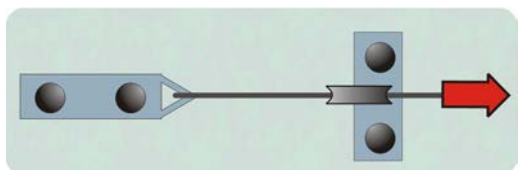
Hauptgruppen-Formen (Wellenhofer)
